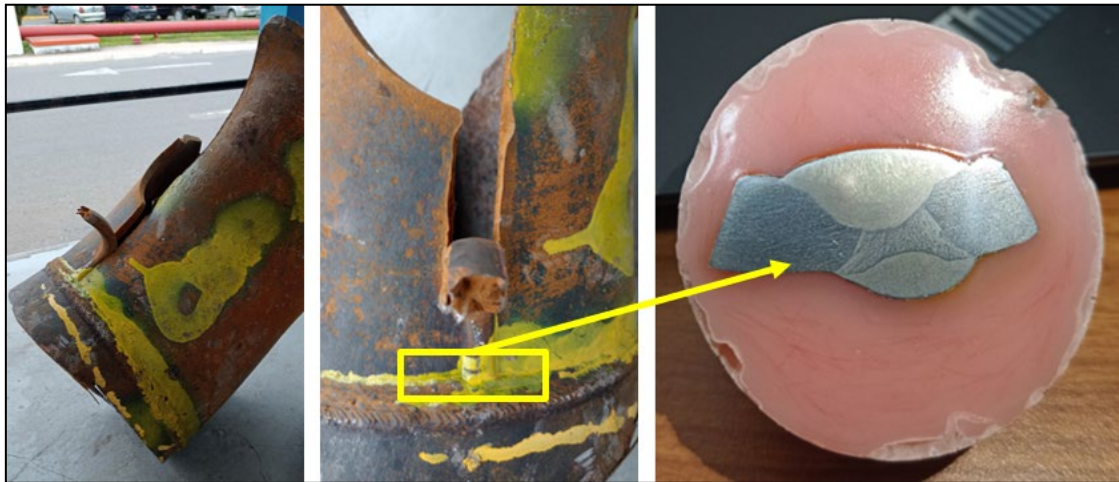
Muestra soldadura – cordón longitudinal – Codo inferior. Corte transversal sobre soldadura no deformada.
